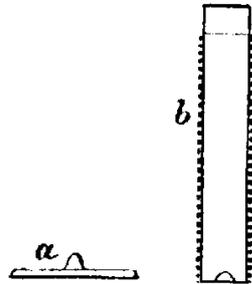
a, rialzo di ferro per caricare le fontane; b - fontana carica
